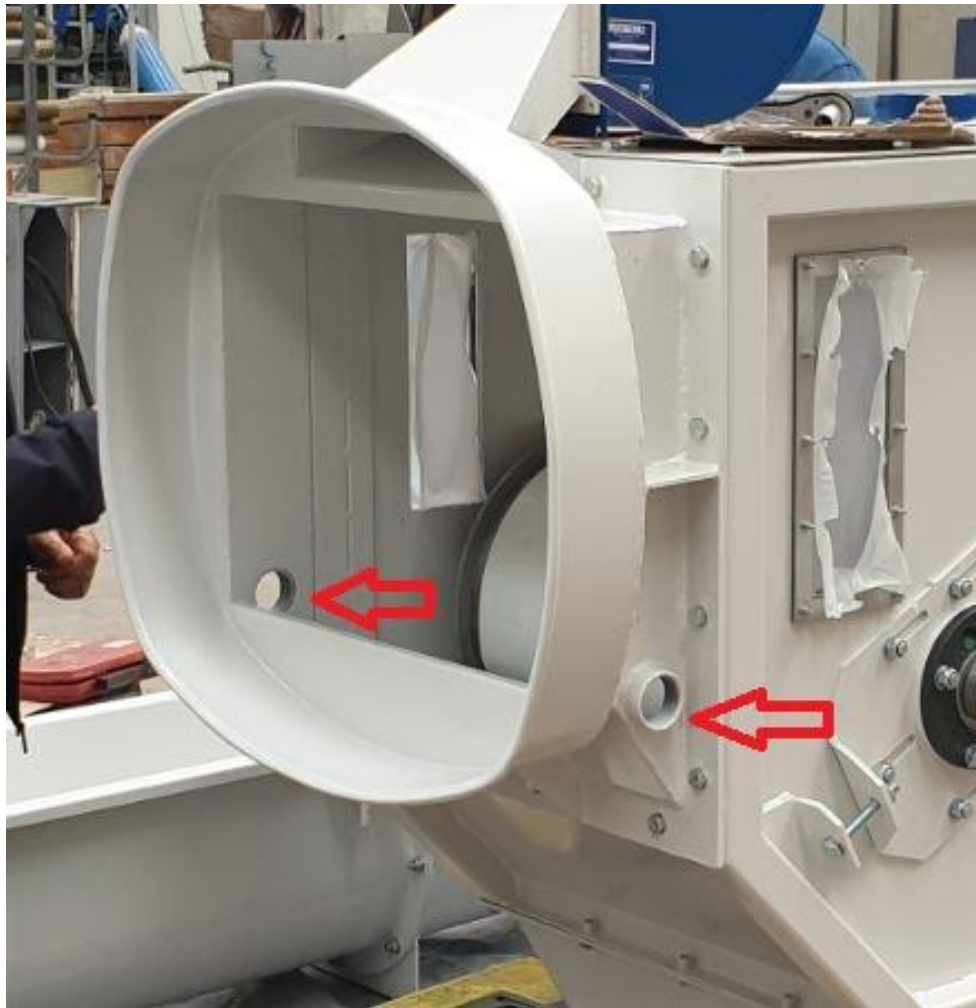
Pormenor para aplicação da sonda de nível máximo do Big-Bag
